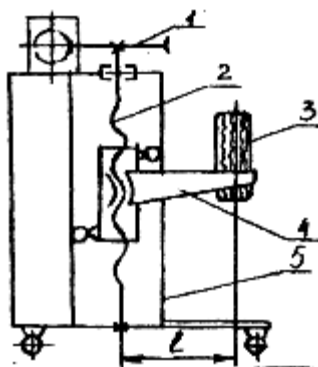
Схема роботи стійки: 1-електромеханічний привод, 2-гвинт; 3-колесо, 4-каретка, 5-стійка
